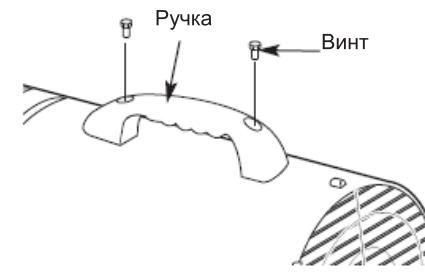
Установка ручки на модель нагревателя ТК-12000, ТК-20000
